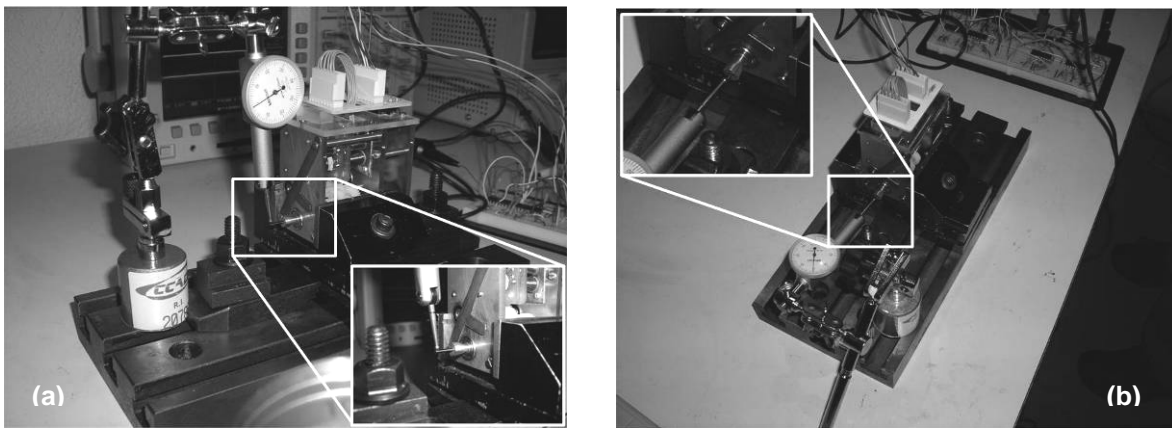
(a) Detalle de prueba de *run-out* radial, (b) Detalle de prueba de *run-out* axial.
